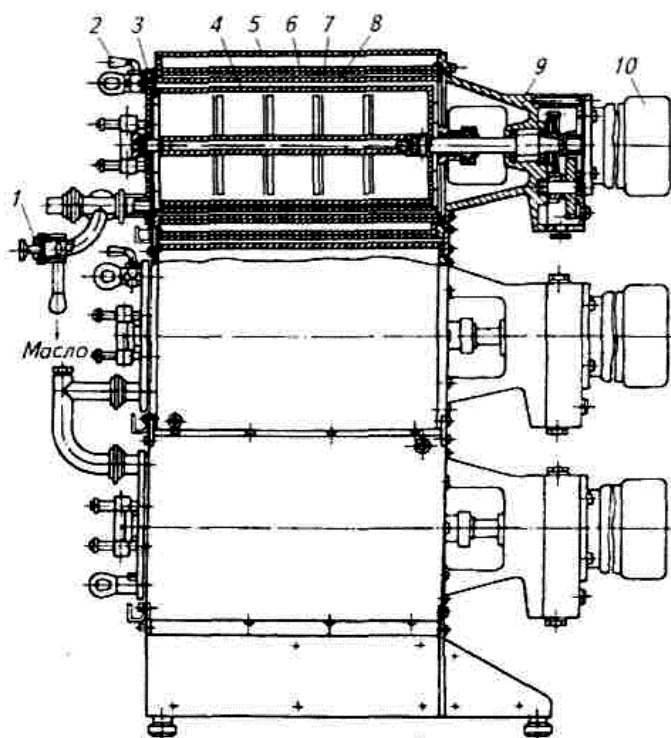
Цилиндрический маслообразователь: 1 - выходной регулирующий кран; 2 - кран для удаления воздуха; 3 - крышка; 4 - вытеснительный барабан; 5 - кожух; 6 - наружная обечайка цилиндра; 7 - спираль; 8 - внутренняя обечайка цилиндра; 9 - редуктор; 10 - электродвигатель
